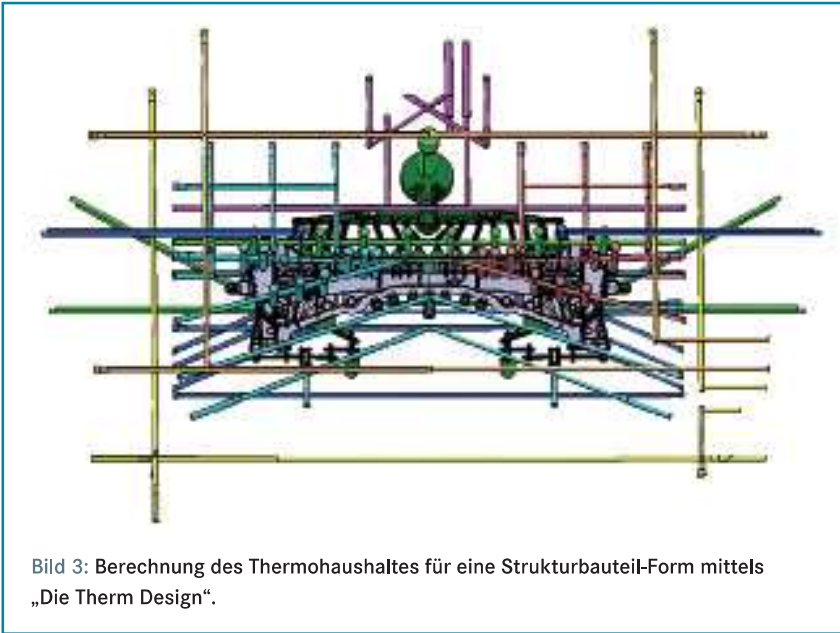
Berechnung des Thermohaushaltes für eine Strukturbauteil-Form mittels „Die Therm Design“.
